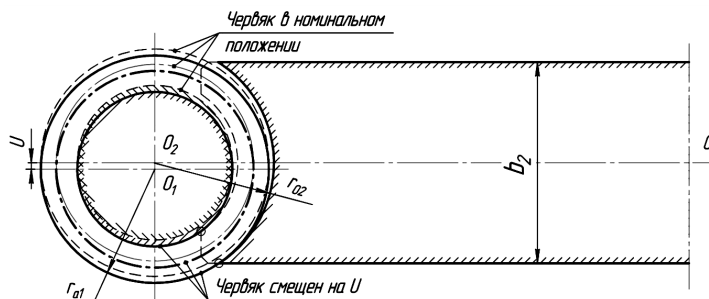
Конструкция передачи с обнулением боковых зазоров
